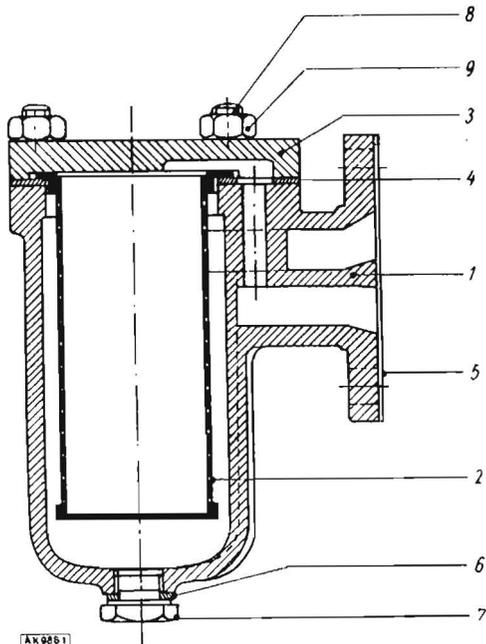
Schmierölfilter ab Motor-Nr. 47113
